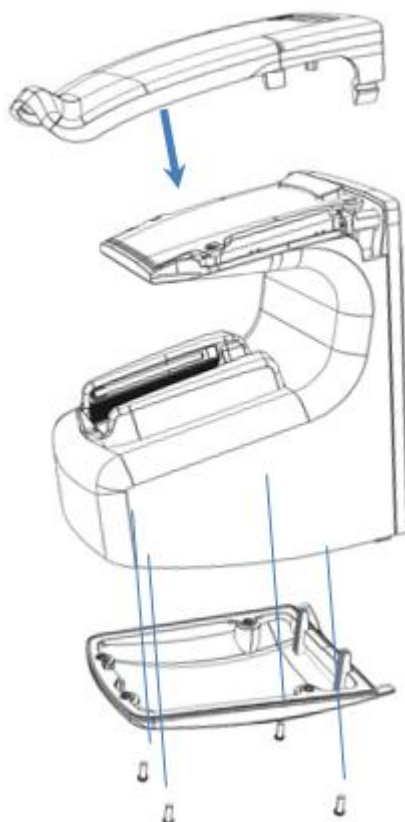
Assemblage de la visière et vissage de la trappe inférieure
